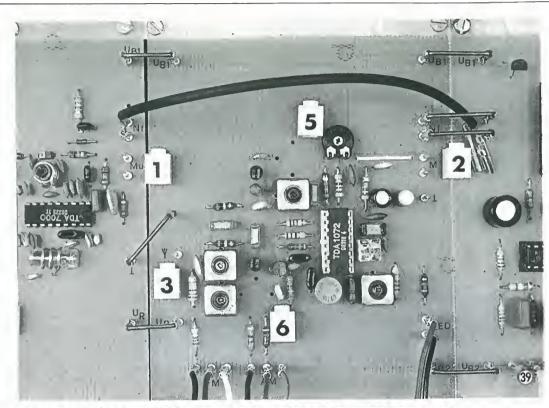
A sinistra della foto è visibile il ricevitore FM completo e collegato agli altri moduli.
